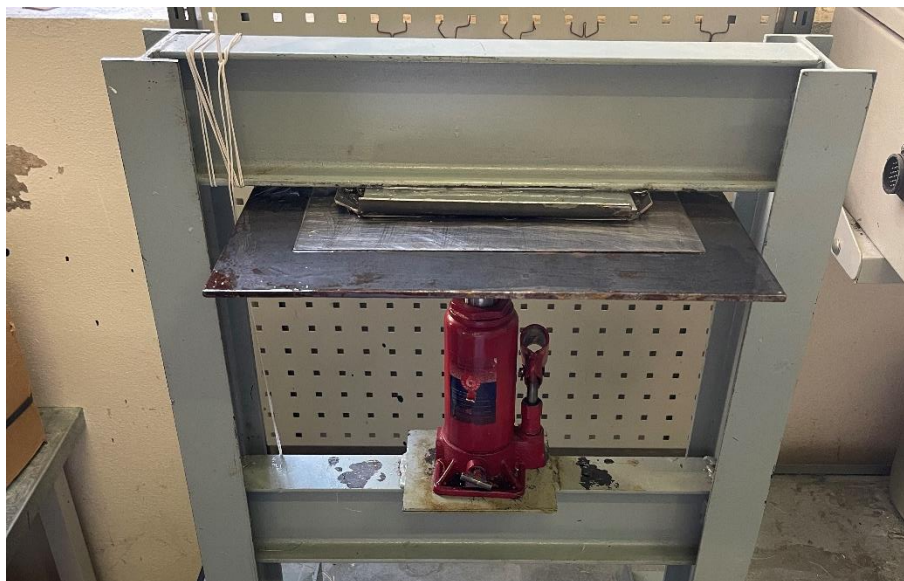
Montagem do molde de compósito sob pressão no macaco hidráulico.
